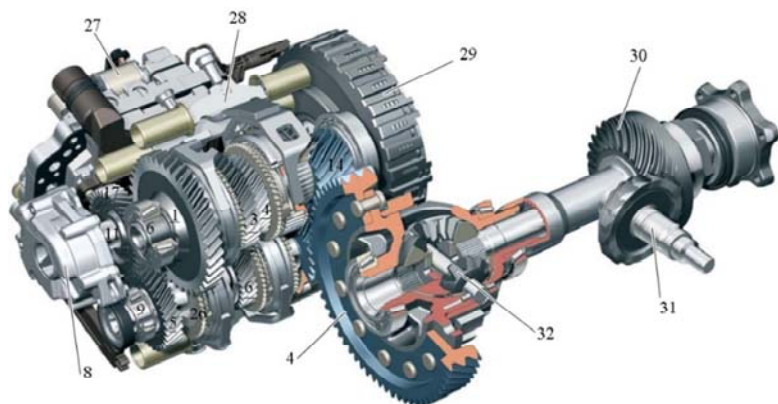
Роботизированная коробка с угловым редуктором:
